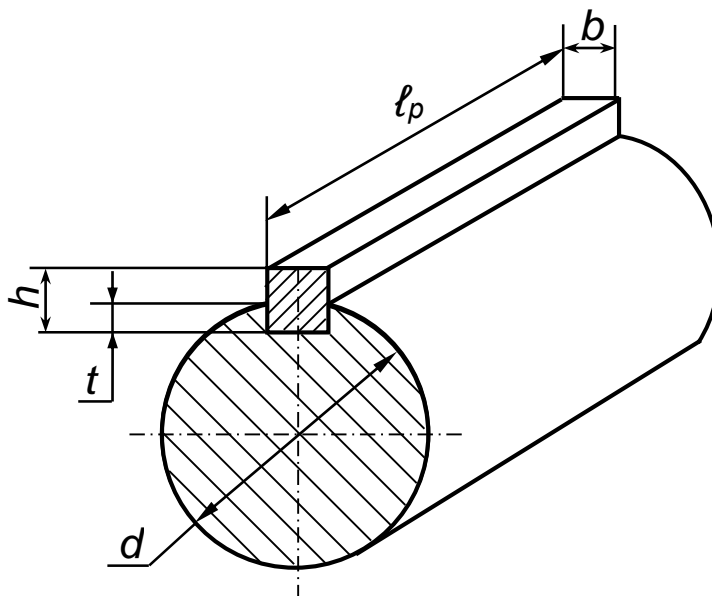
Розрахункова схема шпонкового з'єднання.
